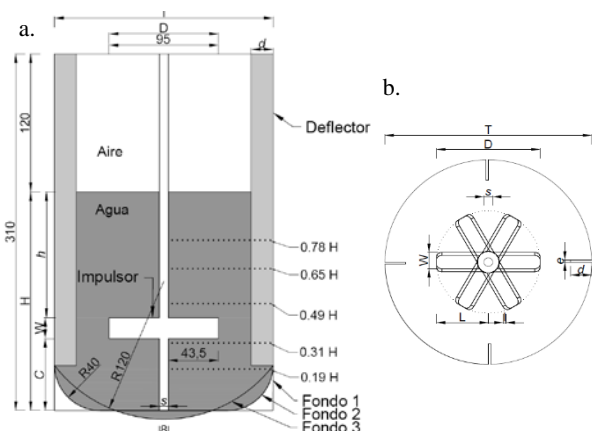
Tanque de mezcla: vista transversal (a) y vista en planta (b).
